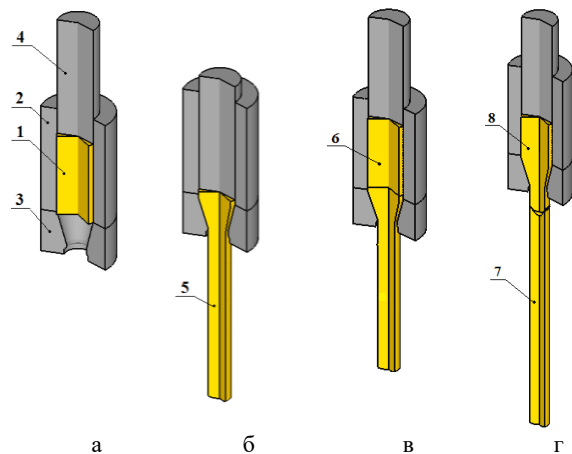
Розрахункові схеми в розрізі на початку та в кінці видавлювання першої та другої заготовок
